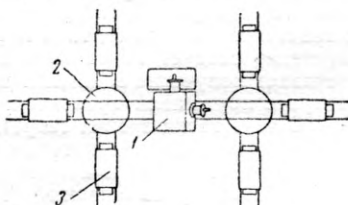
Схема работы на станке ВС-45 с шестью сборочными приспособлениями:
